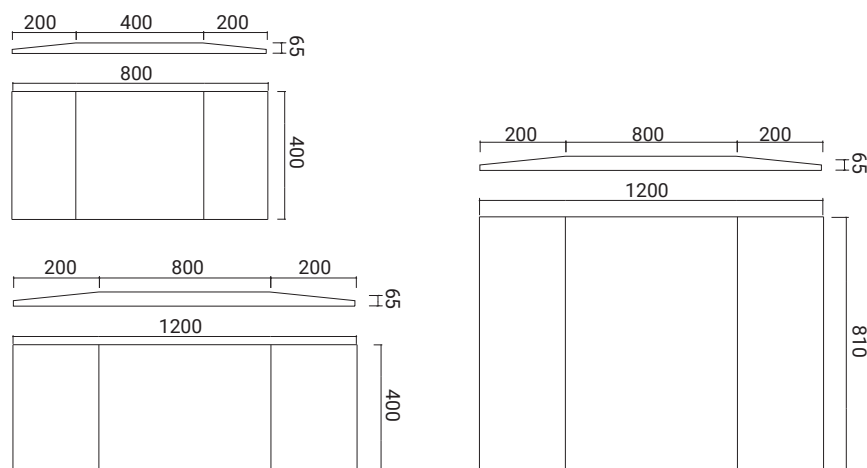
Dimensioni formati disponibili del pannello acustico in mm
